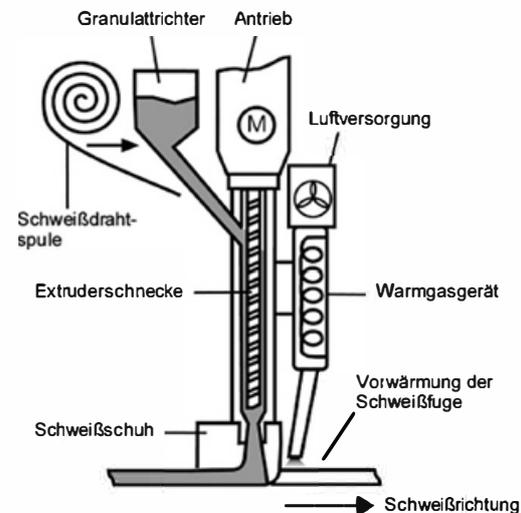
Schema kontinuierliches Schweißen mit Maschinenvariante I.
